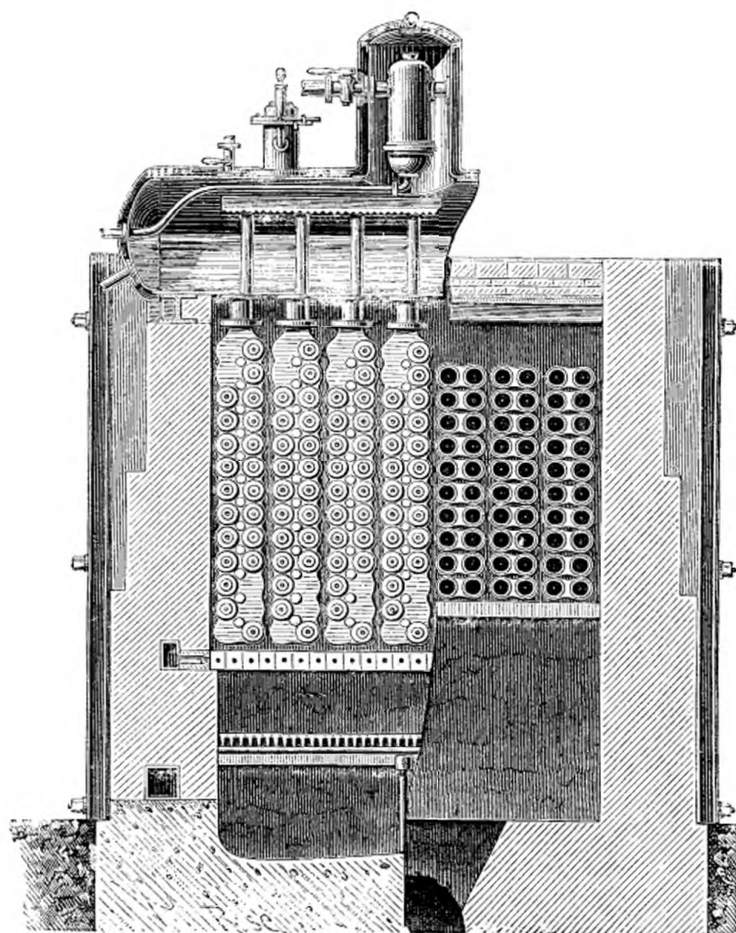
GÉNÉRATEUR LENCAUCHEZ, COUPE TRANSVERSALE
